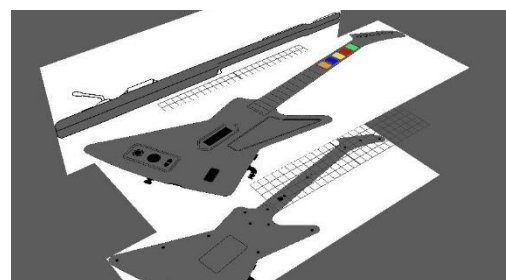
Side-Form, Top-Form und Bottom-Form
